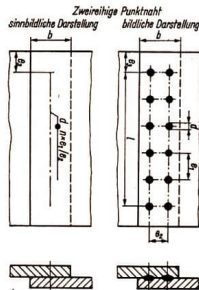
Schweißzeichnung (Preßschweißung), nach [4]
